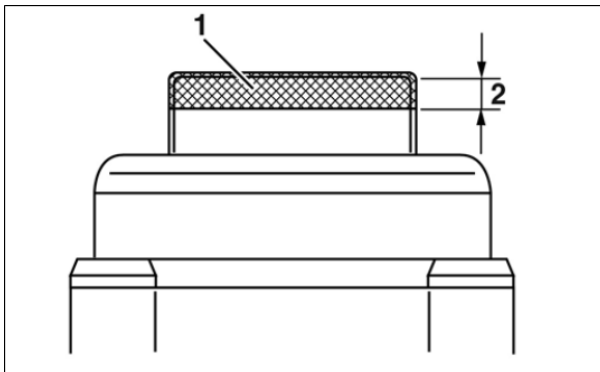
Zona de pintado para el borde cilíndrico de la membrana del sensor
